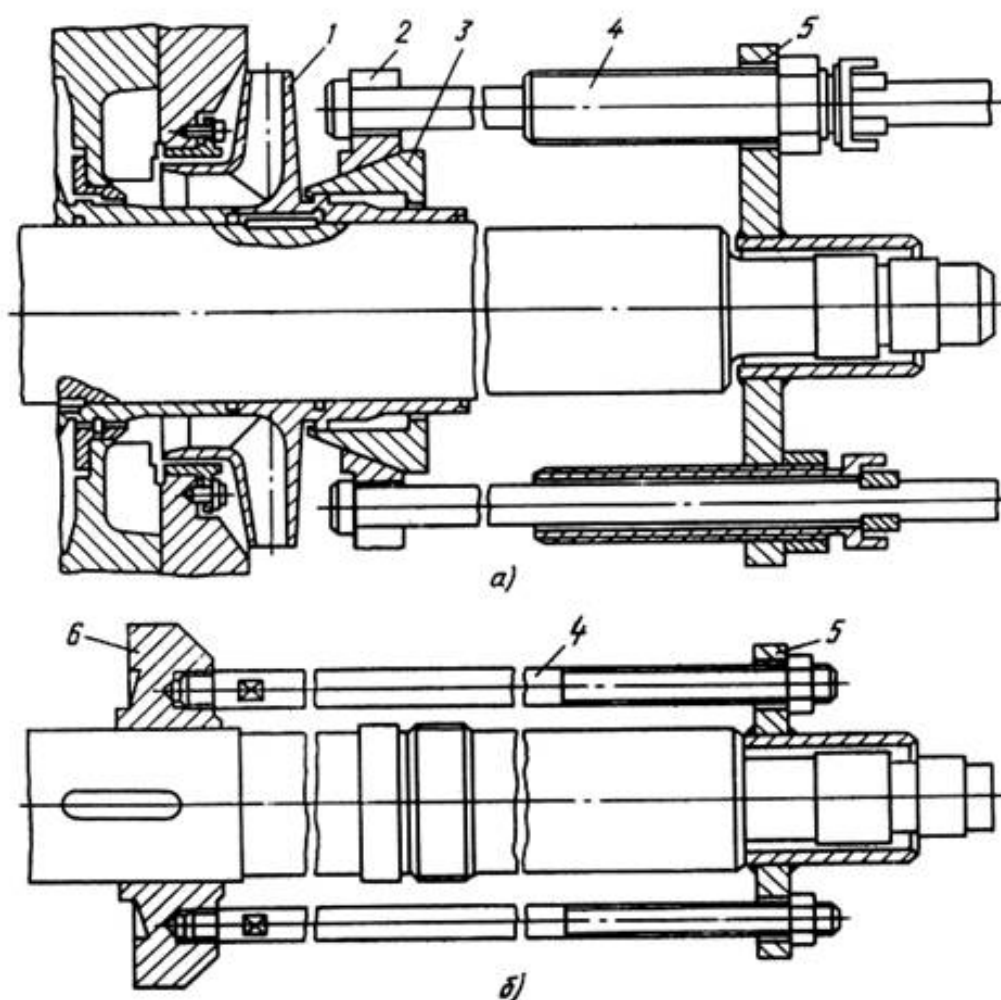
Приспособления для снятия деталей с вала насоса: *а* – для снятия рабочих колес и защитных втулок; *б* – для снятия разгрузочного диска; 1 – рабочее колесо; 2 – кольцо; 3 – захваты; 4 – шпильки; 5 – фланец; 6 – разгрузочный диск.
